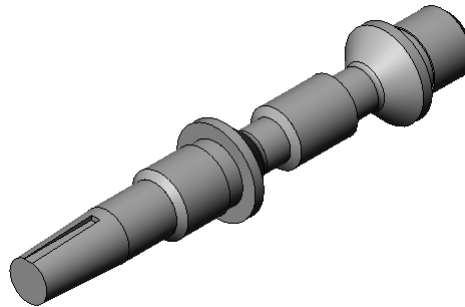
3D модель заготовки черв'яка виконана в Solid Works
